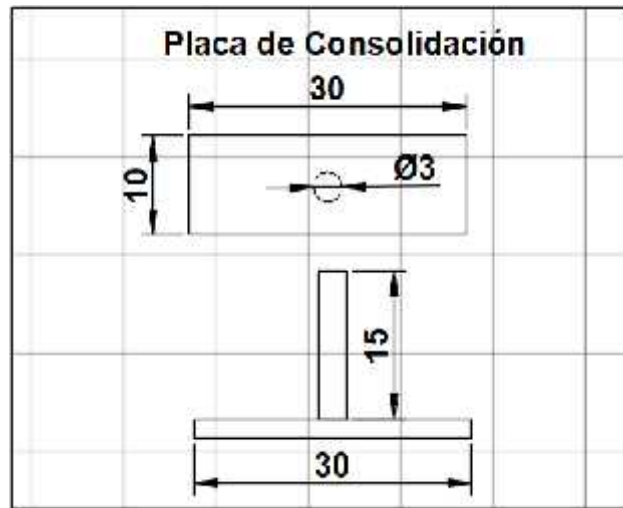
Planos para placa de consolidación, dimensiones en [cm]
